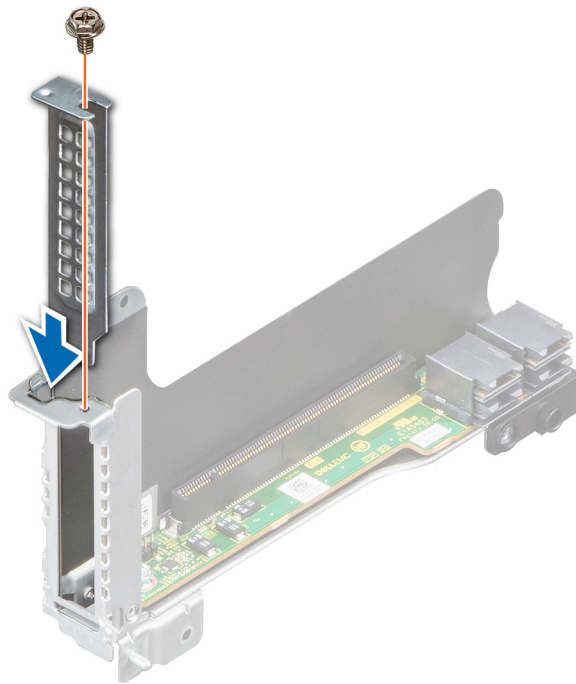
Installation de la plaque de recouvrement de la carte d'extension dans la carte de montage 2
